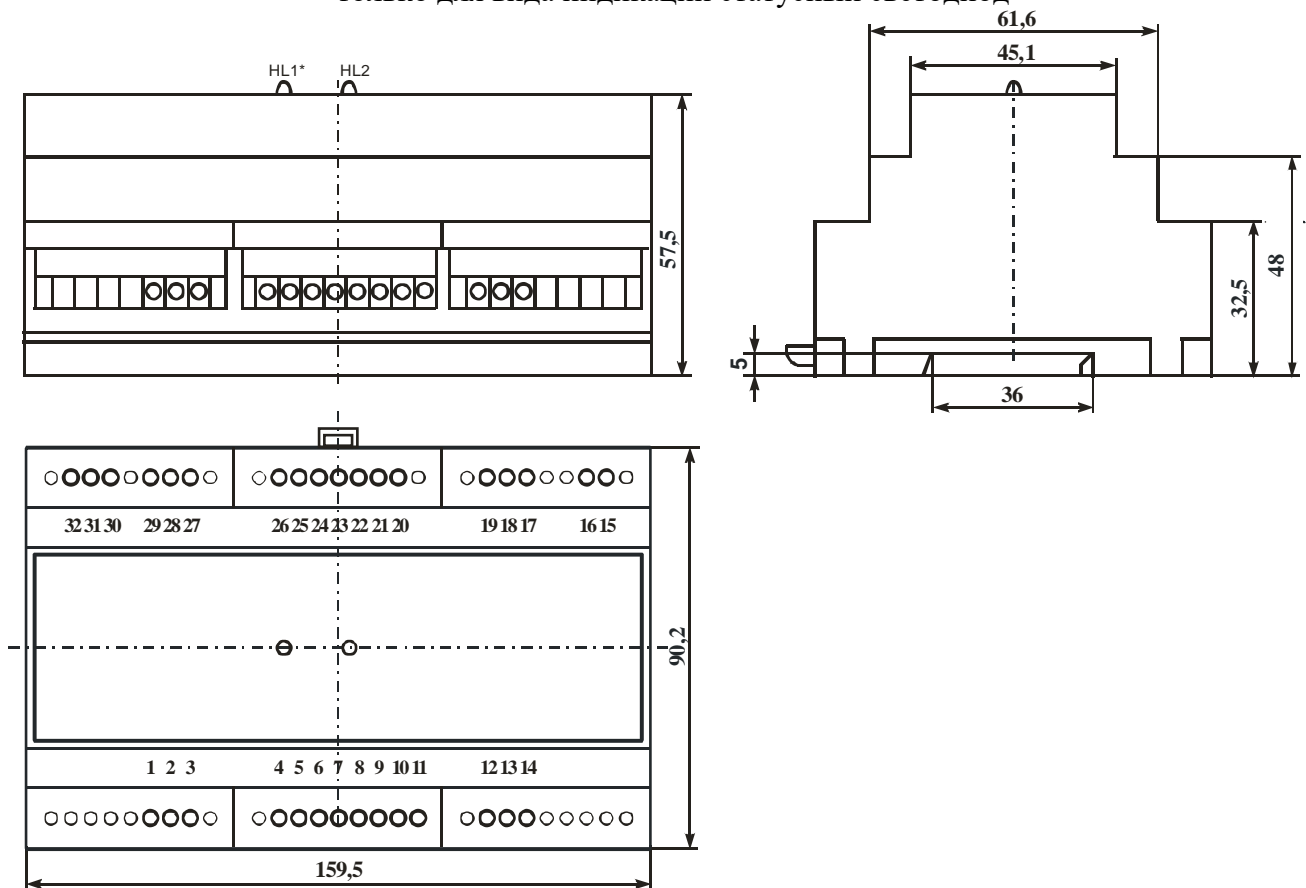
Габаритный чертеж - исполнение 2
